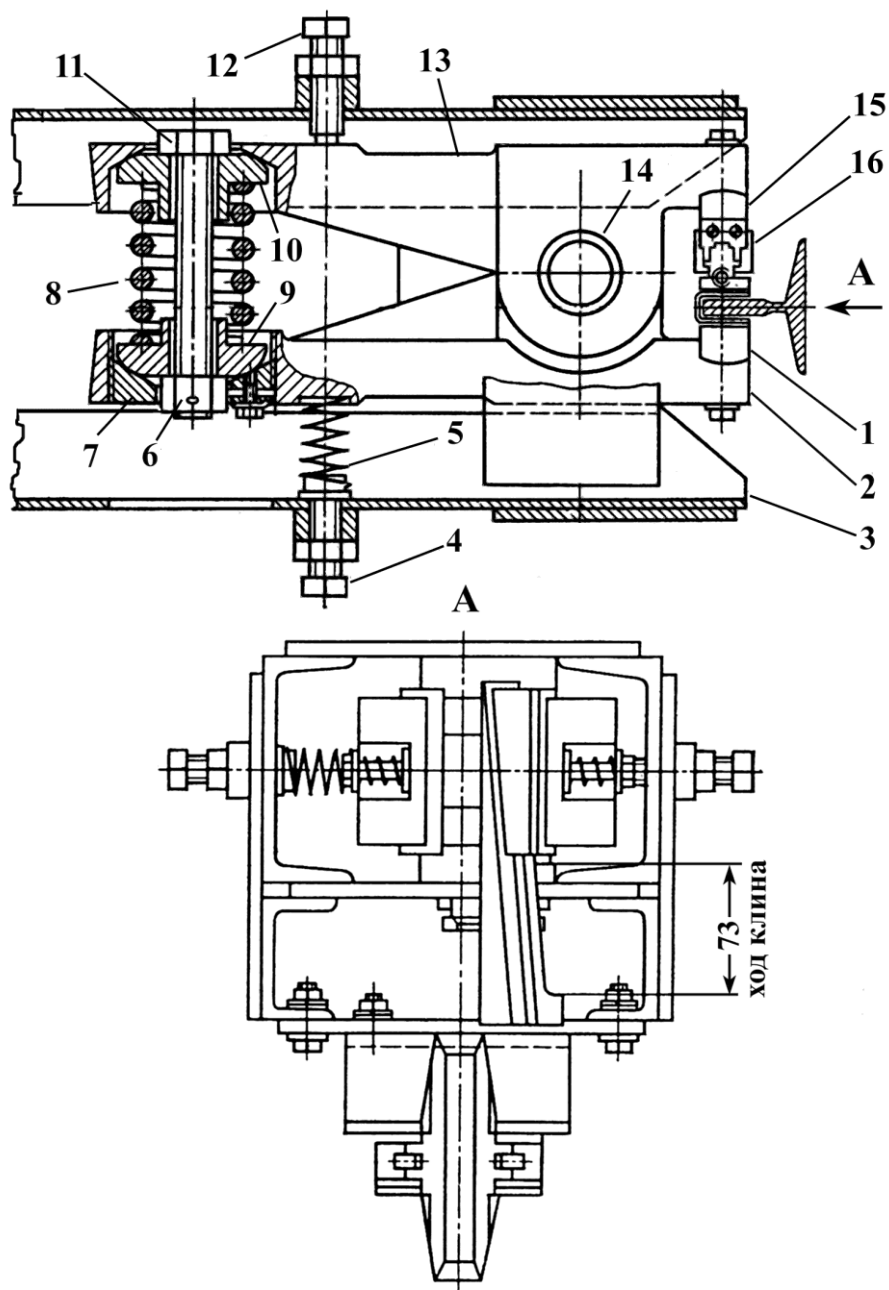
Клещевой односторонний ловитель плавного торможения:
